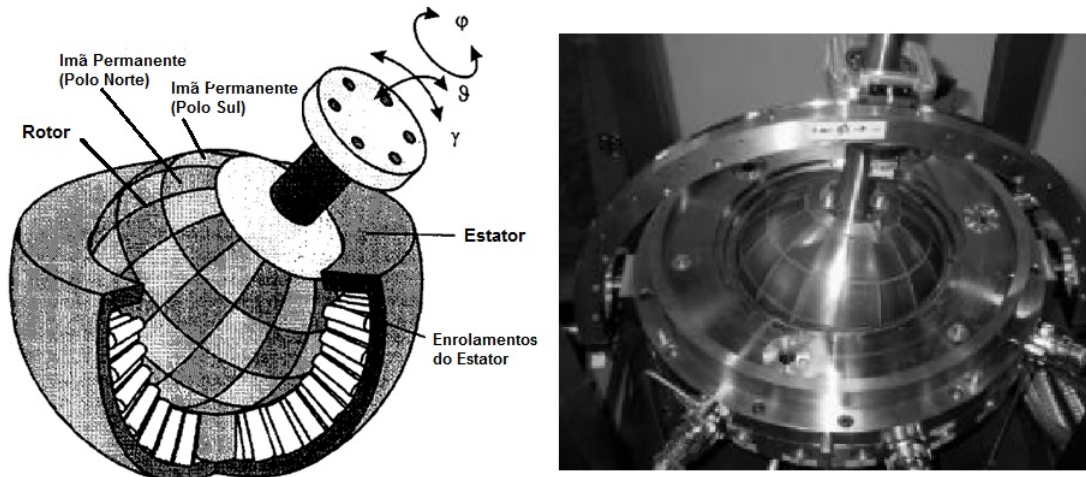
Motor 3-DOF, com múltiplas bobinas.
